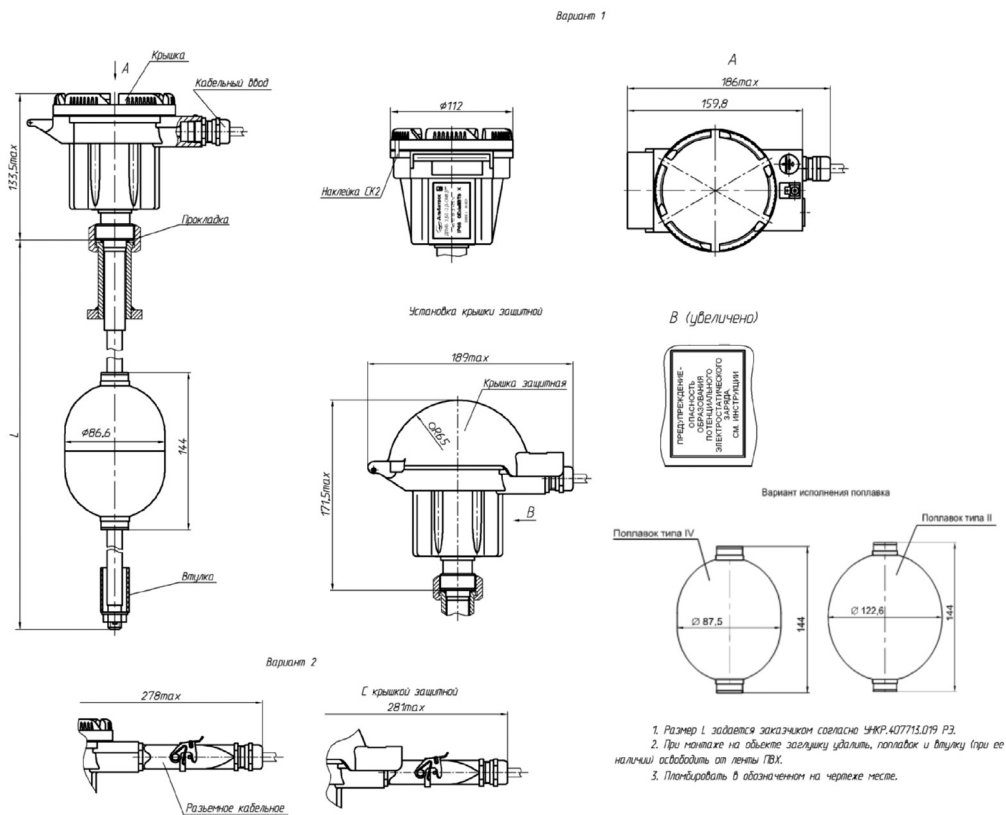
Габаритные размеры датчика ДПУ8
